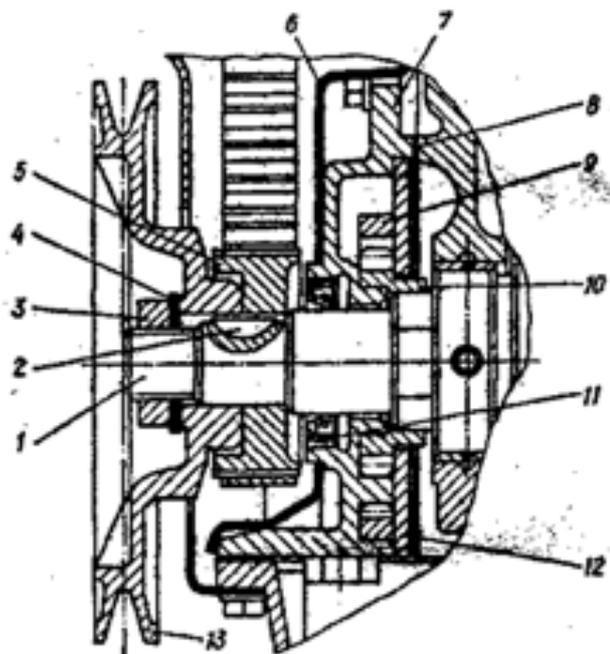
Носок коленчатого вала со шкивом: 1 - вал коленчатый; 2 - шпонка сегментная; 3 - гайка М20х1,5; 4 - шайба; 5 - шкив ведущий коленчатого вала; 6 - внутренний кожух плоскочувчатого ремня; 7 - корпус масляного насоса; 8 - прокладка; 9 и 10 - ведомая и ведущая шестерни масляного насоса; 11 - манжета; 12 - крышка масляного насоса; 13 - шкив привода генератора
